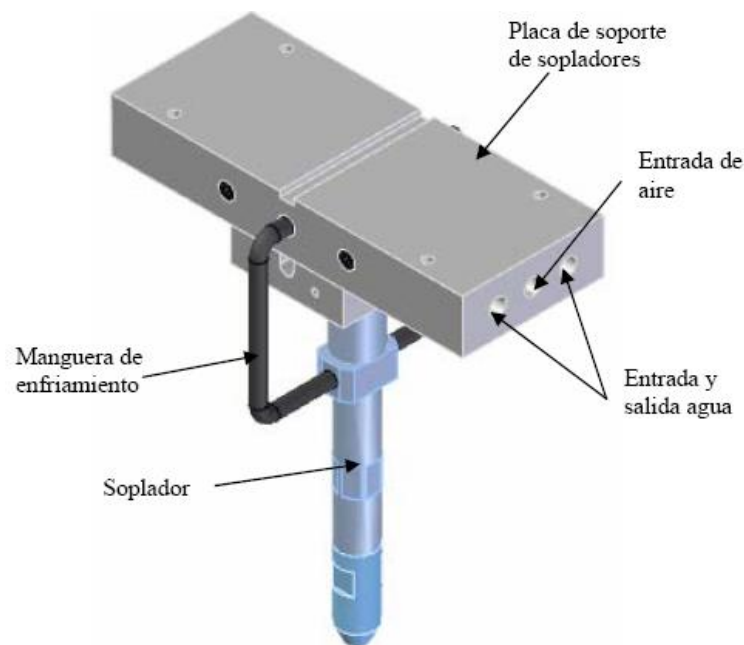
Esquema general del ensamblaje del soplador y la placa soporte
